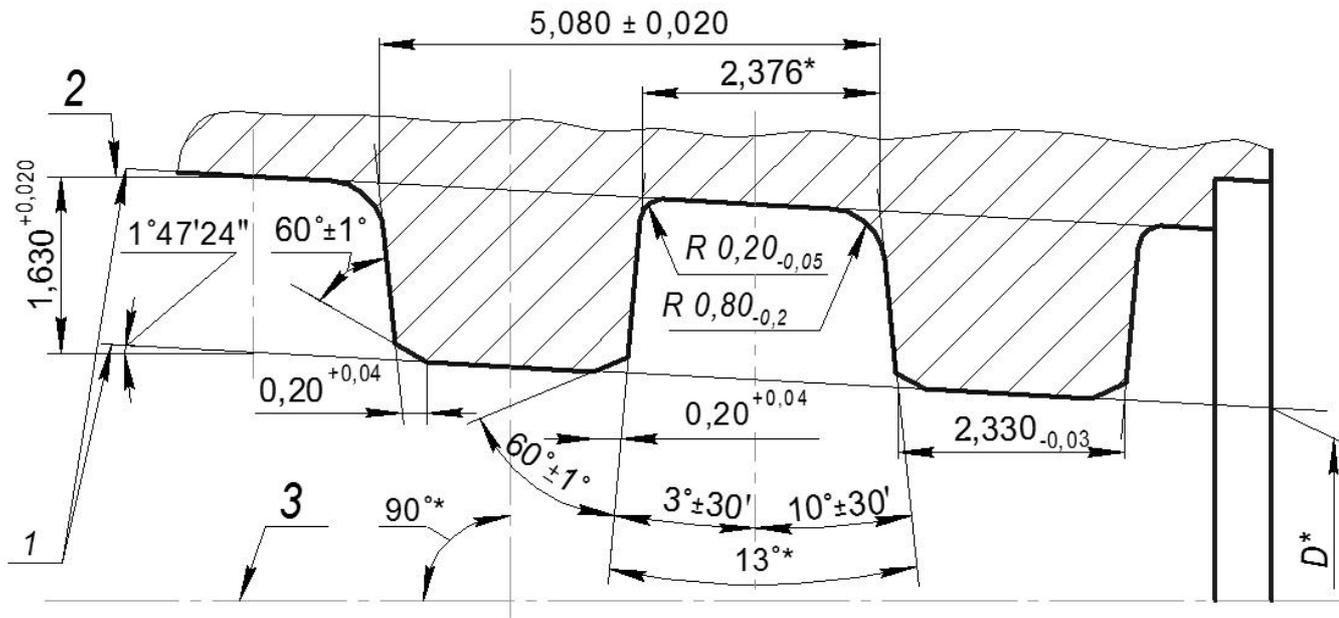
Профиль резьбы калибра-пробки типов Р и К-Р
